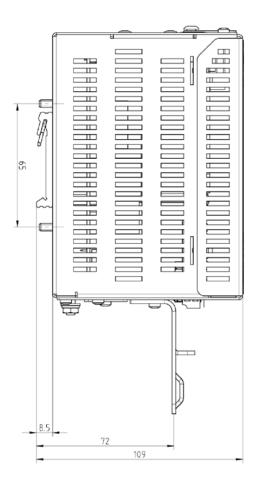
Dessin coté du switch IE X302-7EEC - Vu de côté
